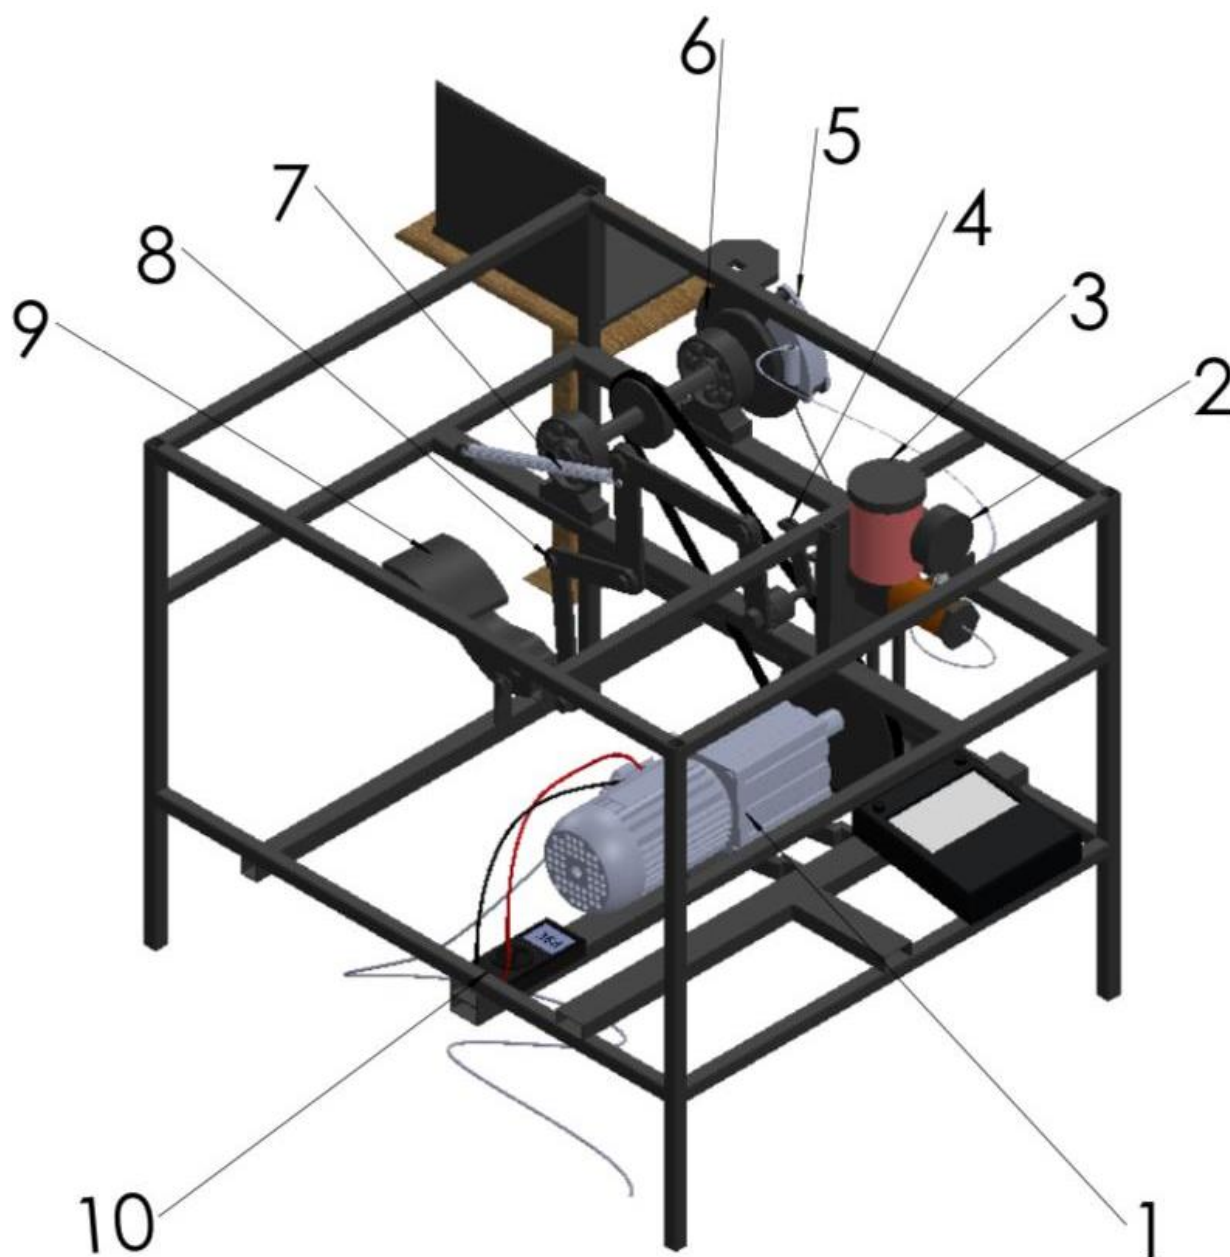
Имитационная 3D модель экспериментального стенда в пакете Solidworks: 1 – Электродвигатель; 2 – Манометр тормозного давления; 3 – Рабочий тормозной цилиндр; 4 – Привод тормозного штока; 5 – Тормозной суппорт; 6 –Тормозной диск; 7 – Пружина тормозного привода; 8 – Тормозной привод; 9 – Тормозная педаль; 10 – Рама
